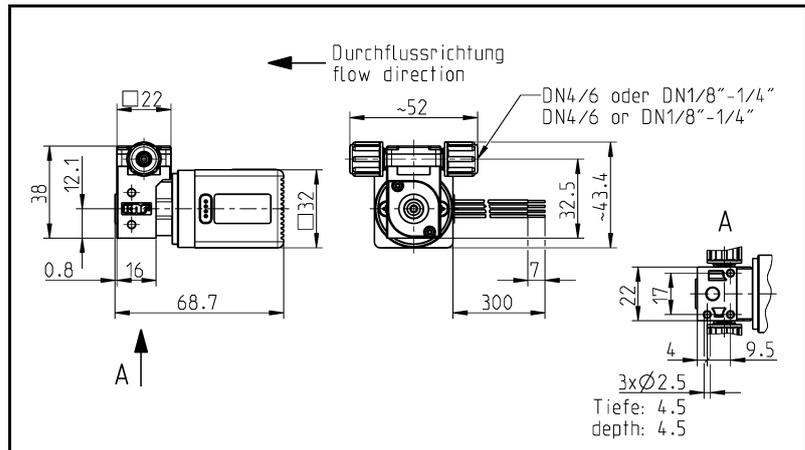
Befestigungsmasse NF 1.25 DCB-4B
